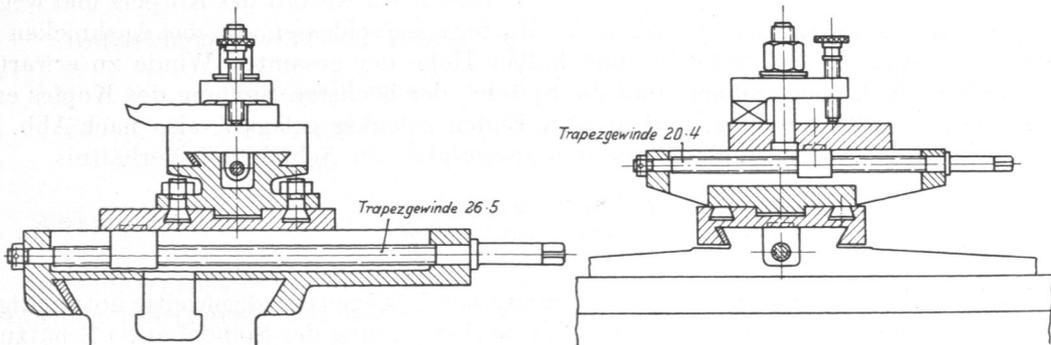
Werkzeugschlitten einer Drehbank. M. 1:10.
